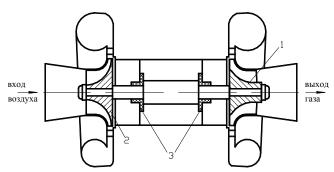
Турбокомпрессор: 7 – рабочее колесо турбины; 2 – колесо компрессора; 3 – подшипники скольжения
